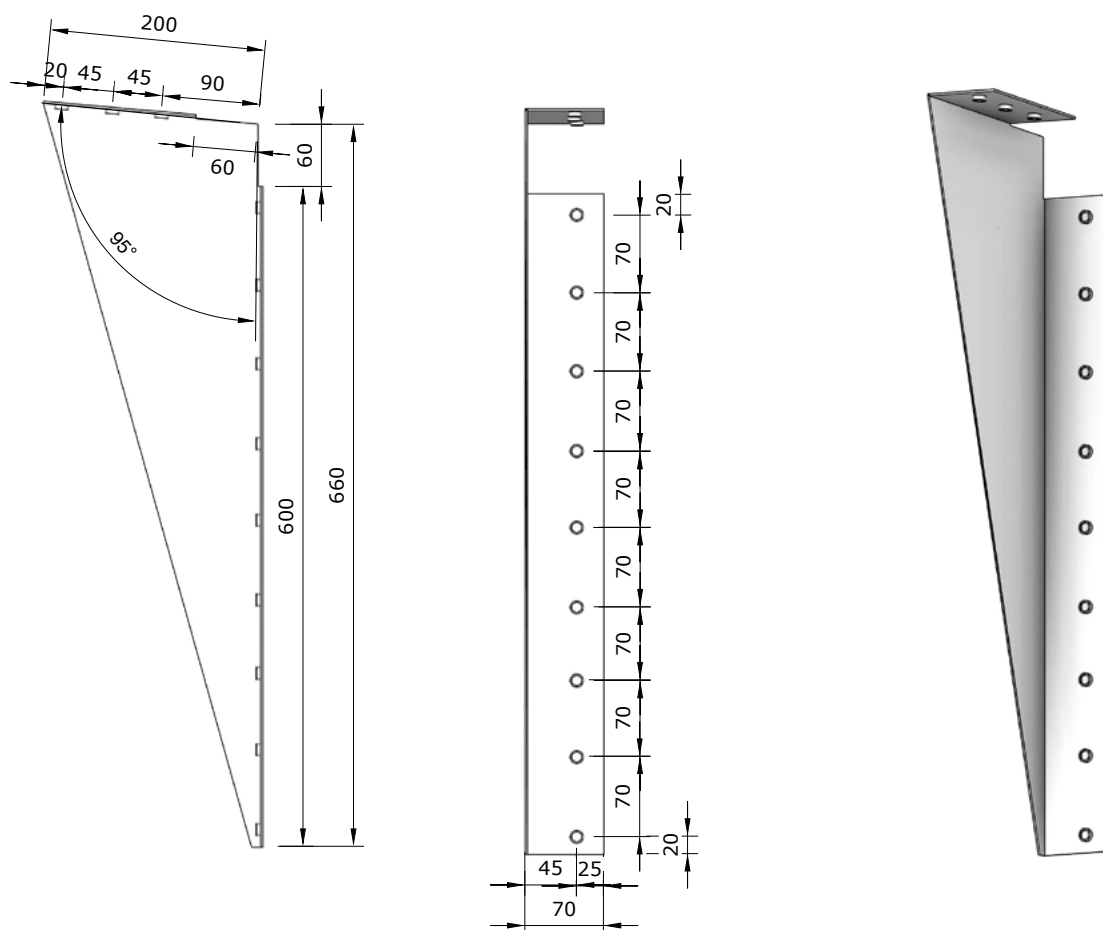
Vues de la tôle de support avec les dimensions de la fixation, dimensions en mm.
